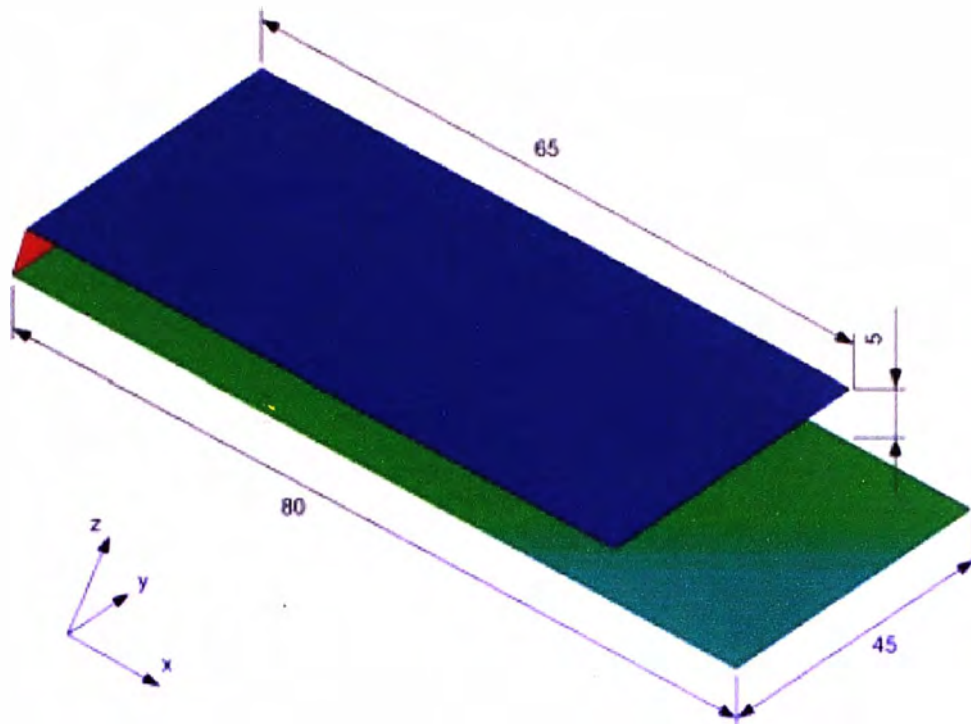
Chasis con dimensiones distintas del teclado y de la pantalla.
